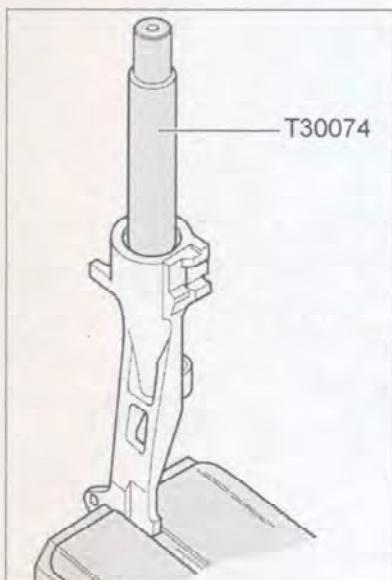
Установка шарикоподшипника в поводок рычага включения передачи заднего хода.
